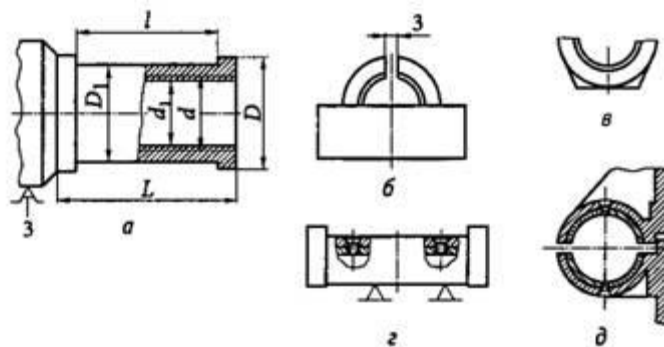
Схема восстановления разъемной (маточной) гайки с бронзовыми вкладышами:
